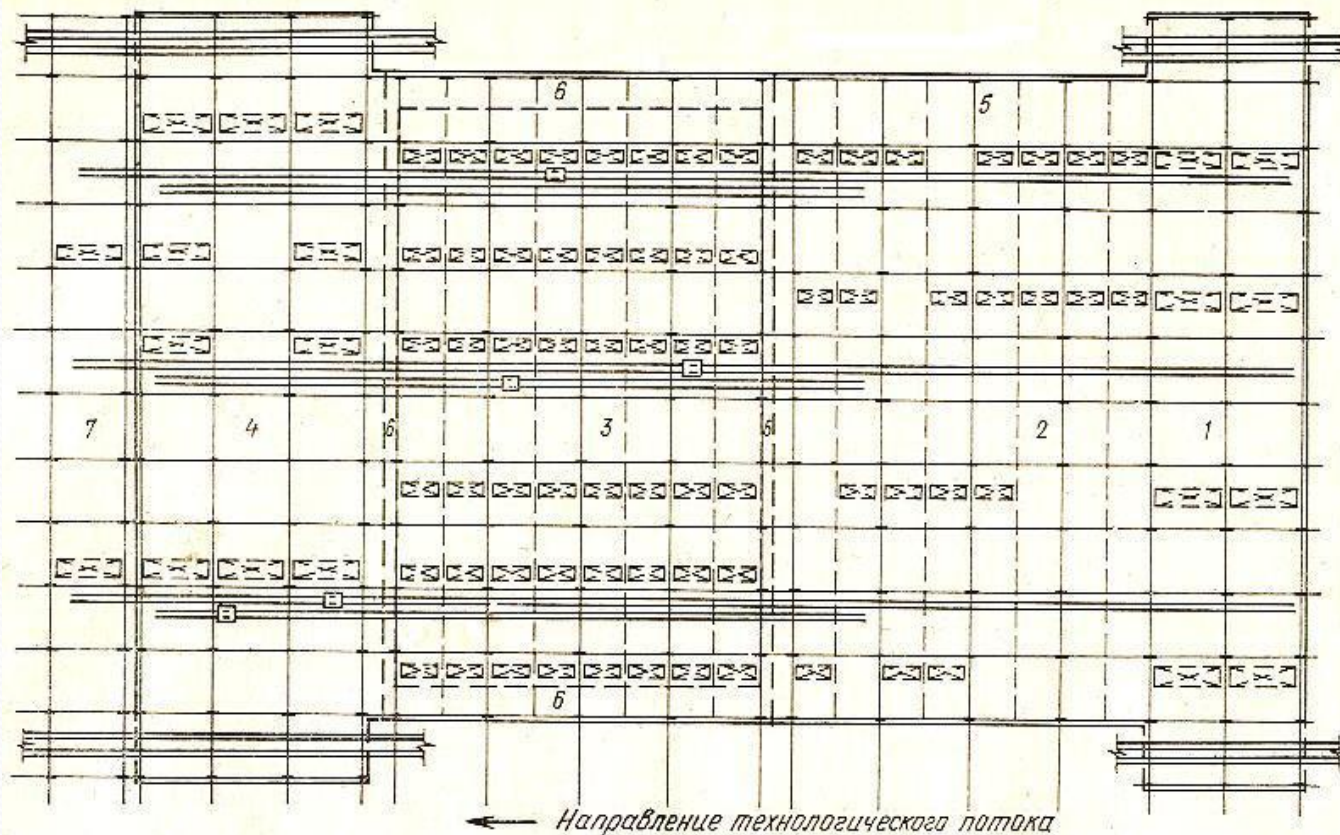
Транспортно-технологическая схема завода с поперечным расположением пролетов: 1- цех подготовки со складом металла; 2 - цех обработки со складом полуфабриката; 3 - цех сборно-сварочный; 4 - цех малярно-погрузочный; 5 - ремонтно-механический цех; 6-бытовые и вспомогательные помещения; 7-открытая эстакада склада готовой продукции
